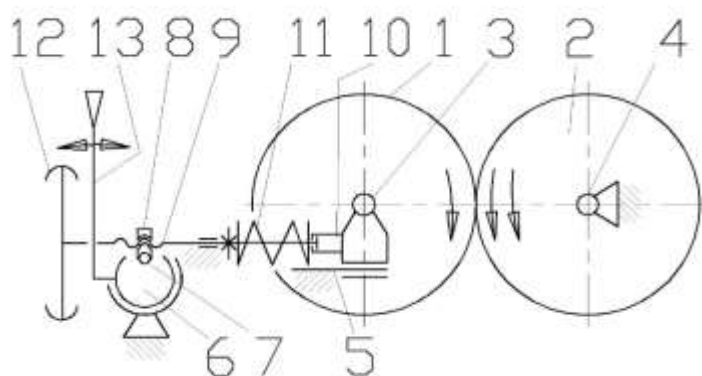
Схема установчого механізму вальцювого верстата.
